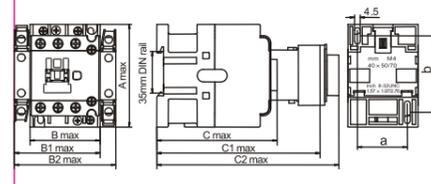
Габаритные и установочные размеры контакторов на токи 6А-38А, мм.
